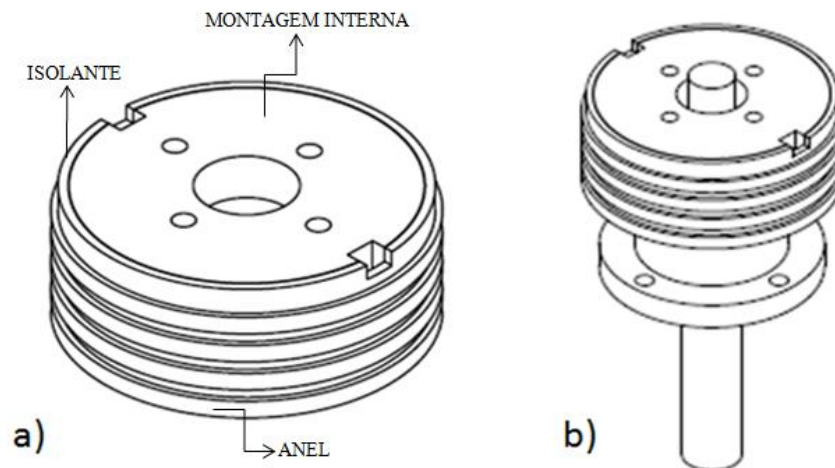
a) Contato Elétrico Rotativo; b) Montagem do contato com o eixo.
